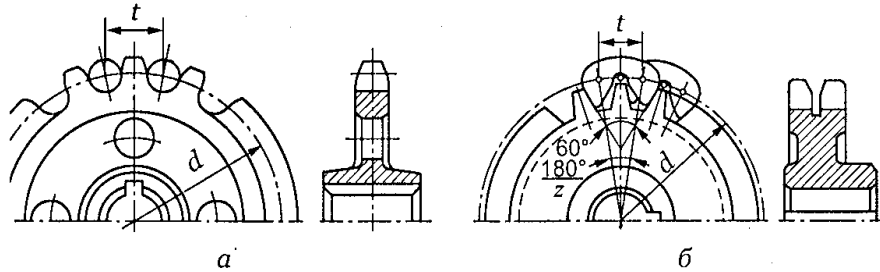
Типы звездочек для цепных передач: а — для втулочной и роликовой цепи; б — для зубчатой цепи
